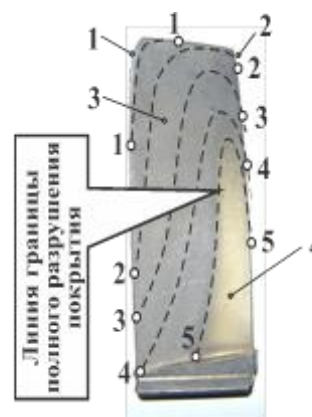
Схема неравномерного износа поверхности (неравномерность 1-го рода) пера лопатки компрессора
